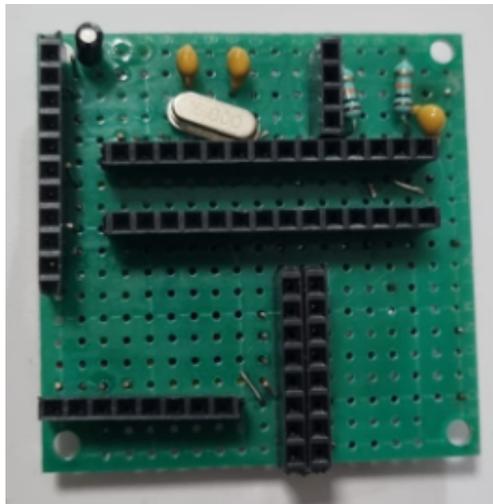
Soldadura de componentes y cableado de placa de sensores
